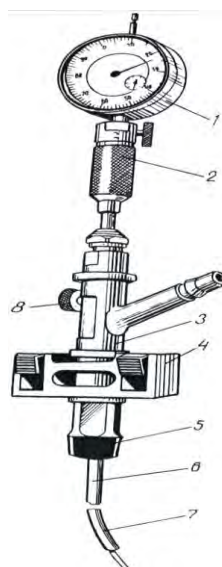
Устройство КИ-11140 ГОСНИТИ для измерения зазоров в КШМ
